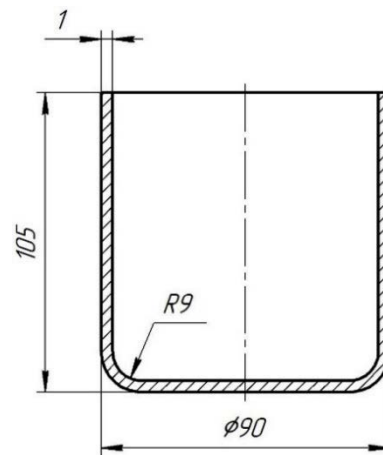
Ескіз напівфабрикату для виготовлення пітчера
